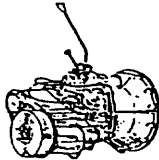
C.2-2. EJES Y ENGRANAJES: 1. Conjunto eje principal
